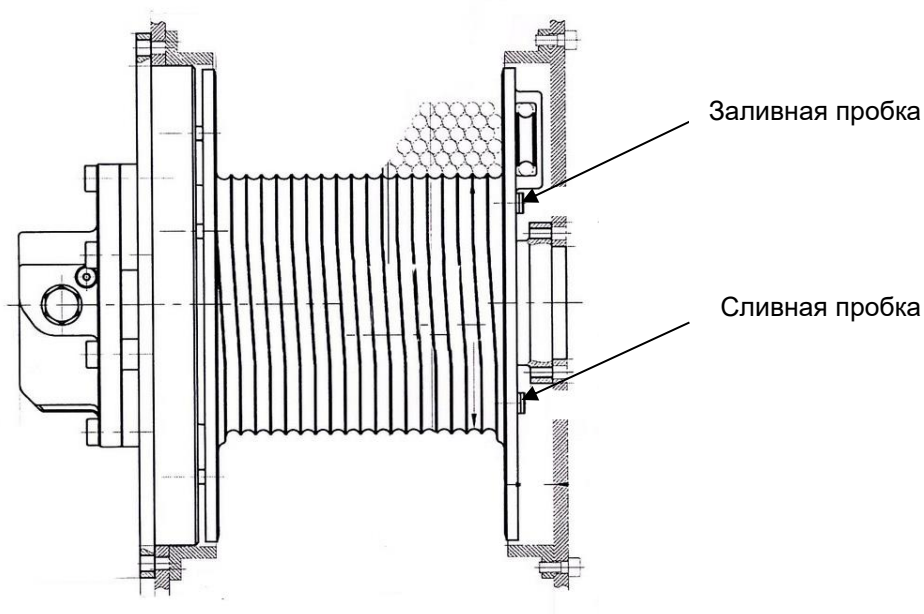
Лебедка с расположением сливной и заливной пробок на боковой (торцевой) поверхности барабана
